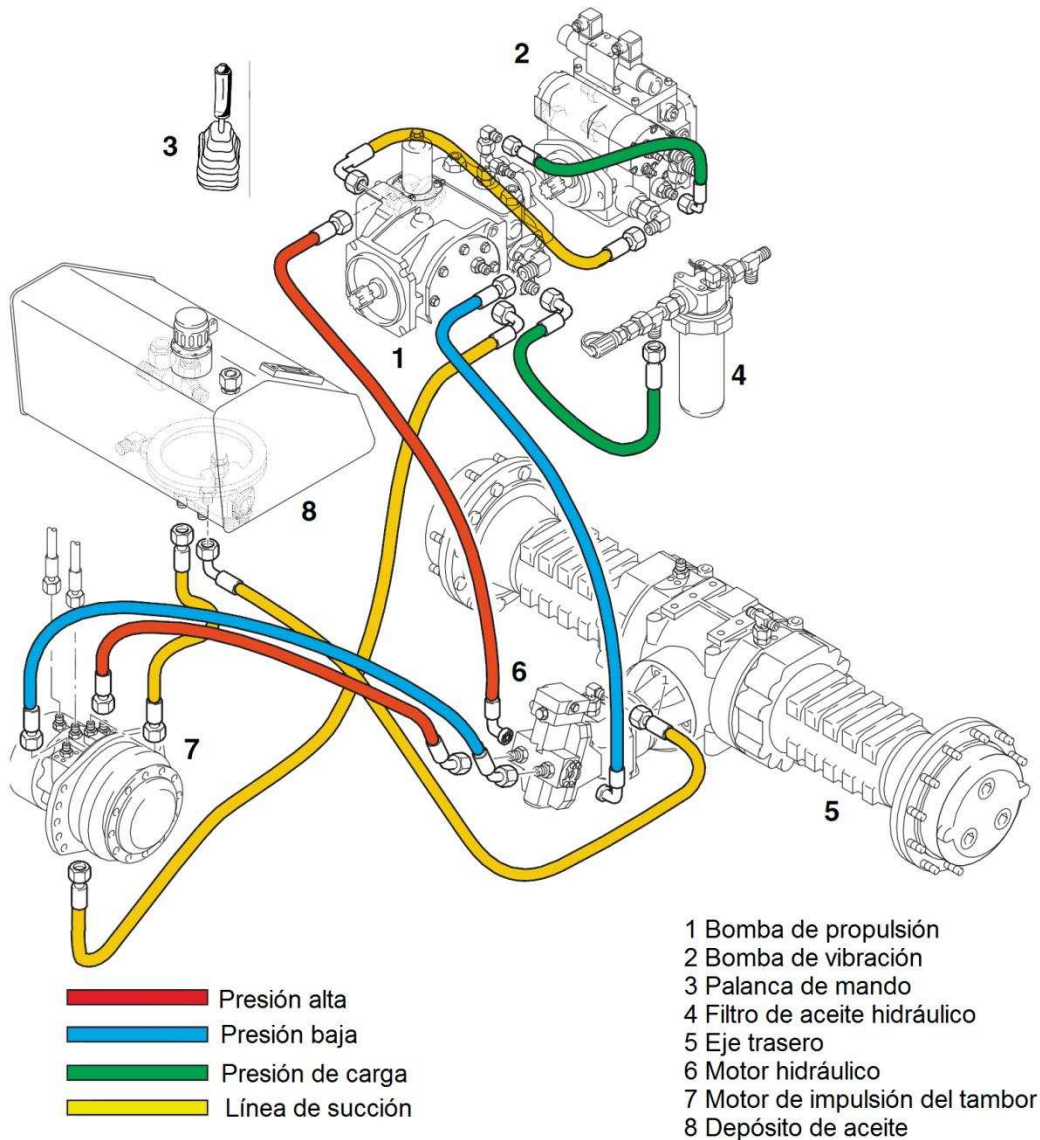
Partes principales de un compactador vibratorio de tambor simple<sup>103</sup>
